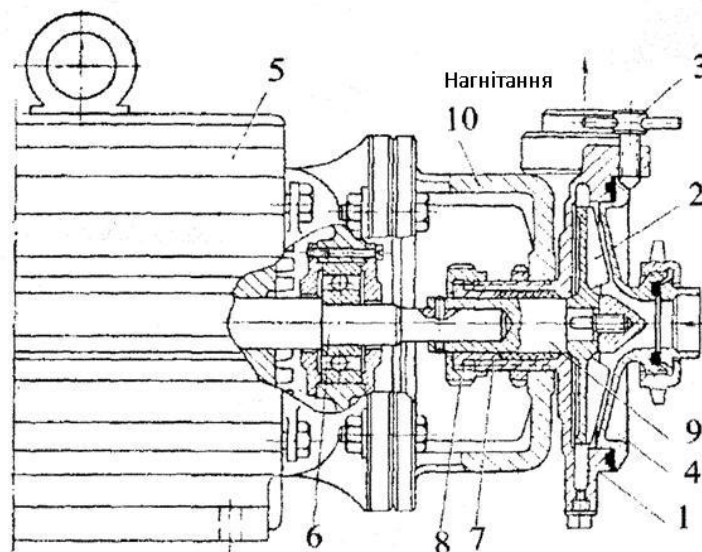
Схема відцентрового насоса: 1 - корпус; 2 - робоче колесо; 3 - гвинт; 4 - кришка; 5 - двигун; 6 - вал; 7 - сальник; 8 - гайка; 9 - насадка; 10 - кронштейн.
